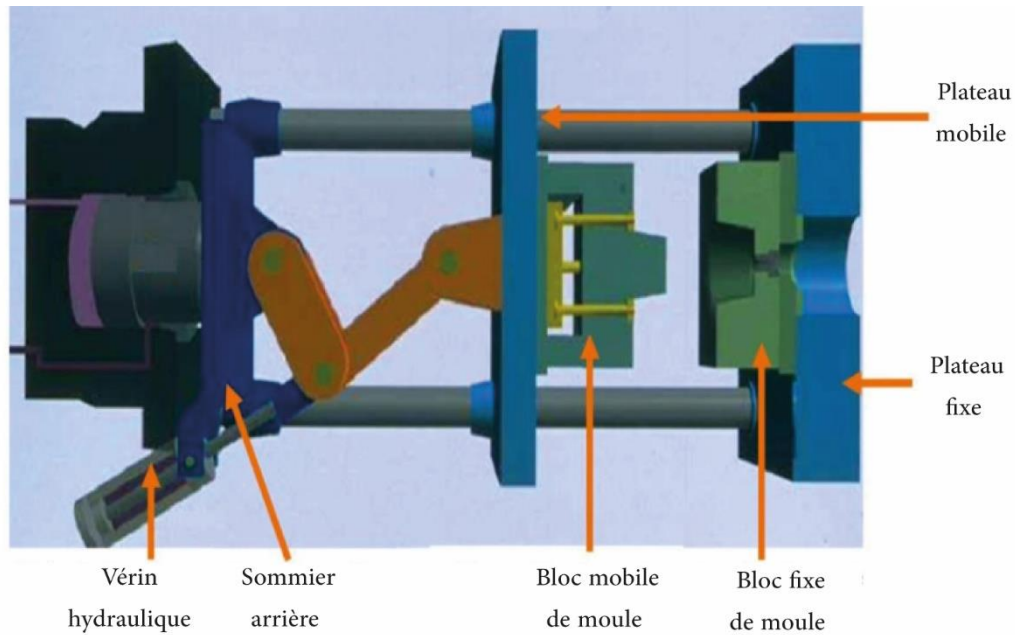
Fermeture Mixte (Hydraulique-Mécanique). [19]
